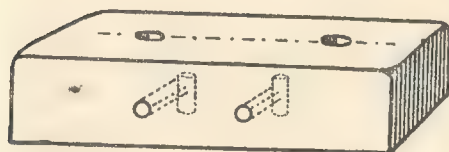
Der Sockel des Detektors mit den sechs Bohrungen.
